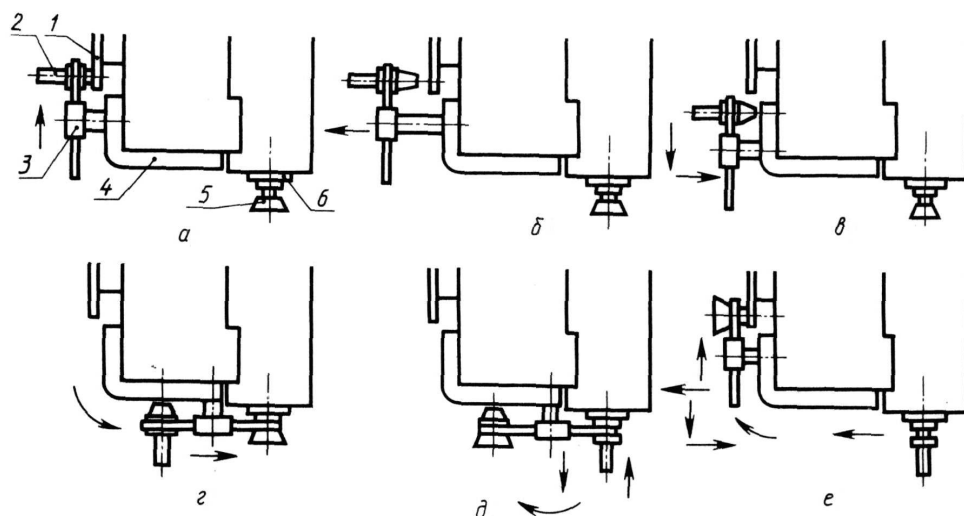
Цикл работы автооператора автоматической смены инструмента:
